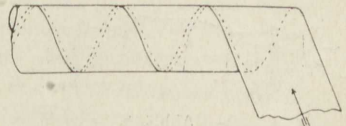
Spiralgeschweißtes Rohr.
